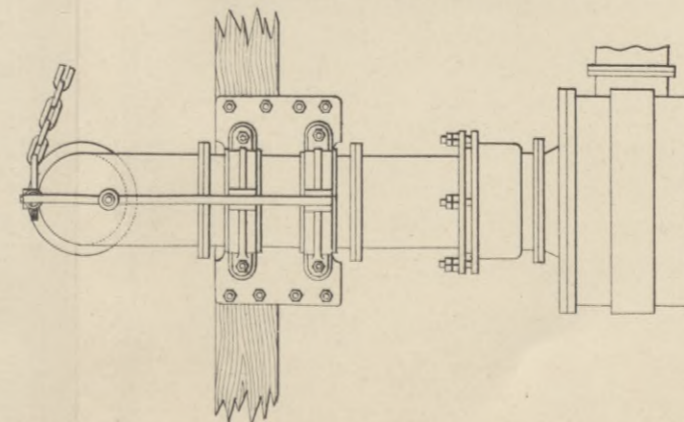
Coupe du presse-étoupe et du manchon d'assemblage de l'arbre.
